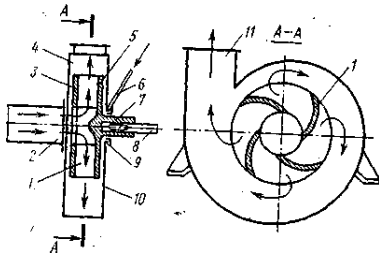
Грунтовий насос: 1 - лопаті; 2 - всмоктуючий патрубок; 3, 5 - диски робочого колеса; 4 - корпус; 5 - трубка для подачі води; 7 - маточина; 8 - вал; 9 - сальникове ущільнення; 10 - кришка корпусу; 11 - відливний канал.
